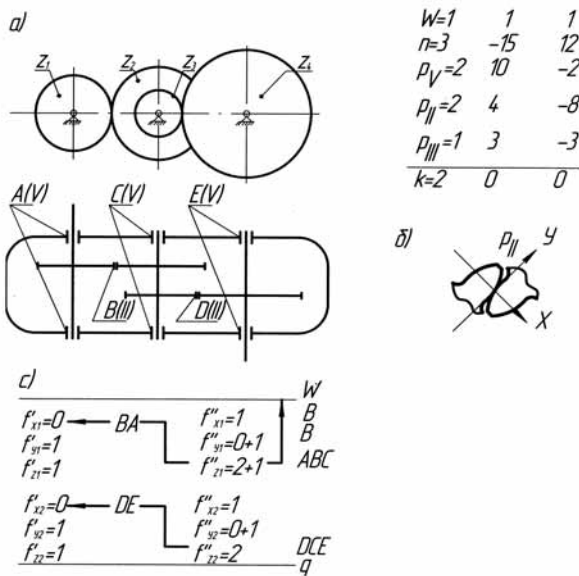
Модернизированный редуктор: а – кинематическая схема; б – контакт зубьев второй ступени редуктора; с – таблица распределения подвижностей в кинематических парах
